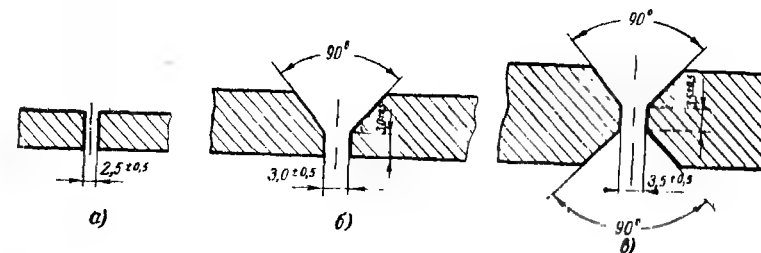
Механическая обработка заготовок короткозамыкающих колец под сварку.
